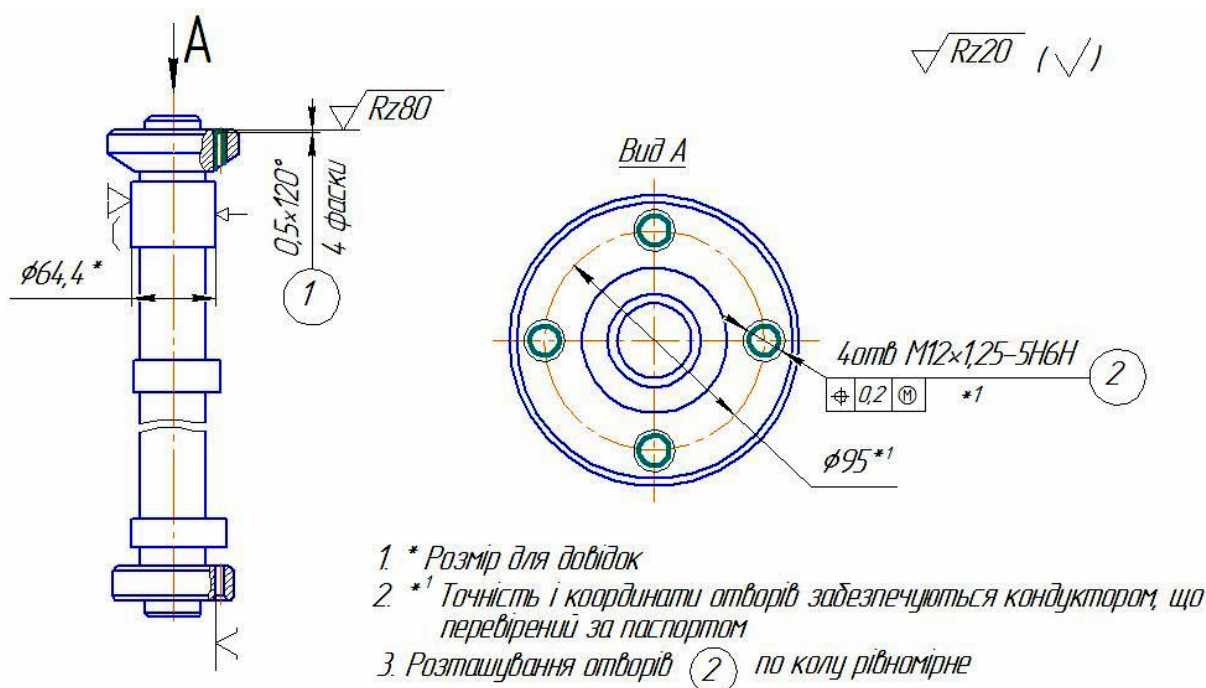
Ескіз радіально-свердлильної операції
